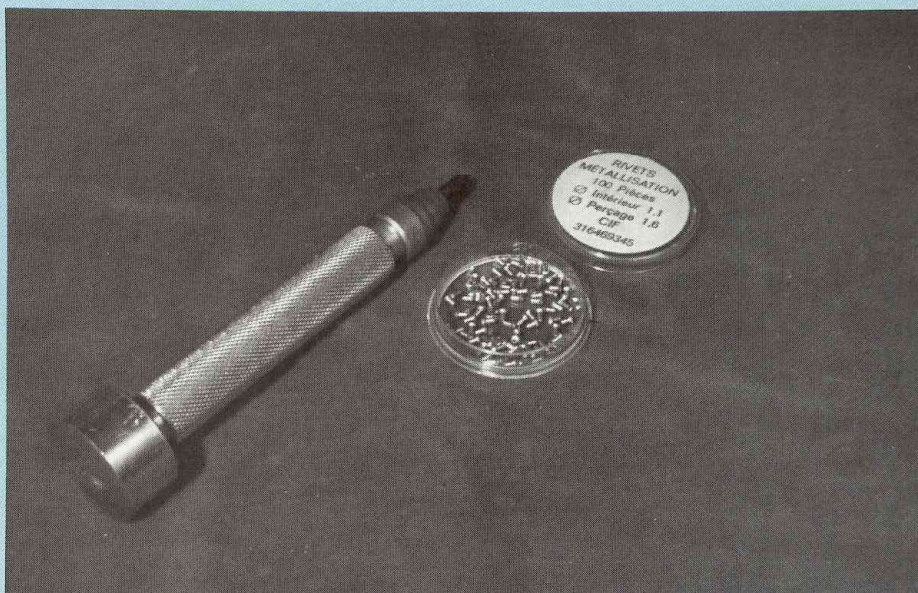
Rivets et outil à riveter. Les rivets ont un diamètre extérieur de 1,1 mm.
